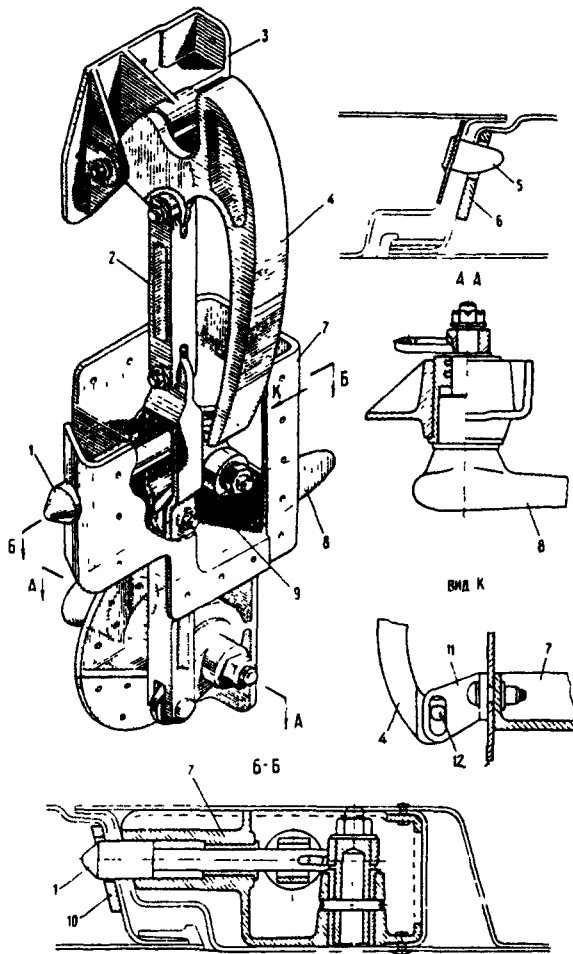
Бортовой аварийный люк (вид снаружи)
